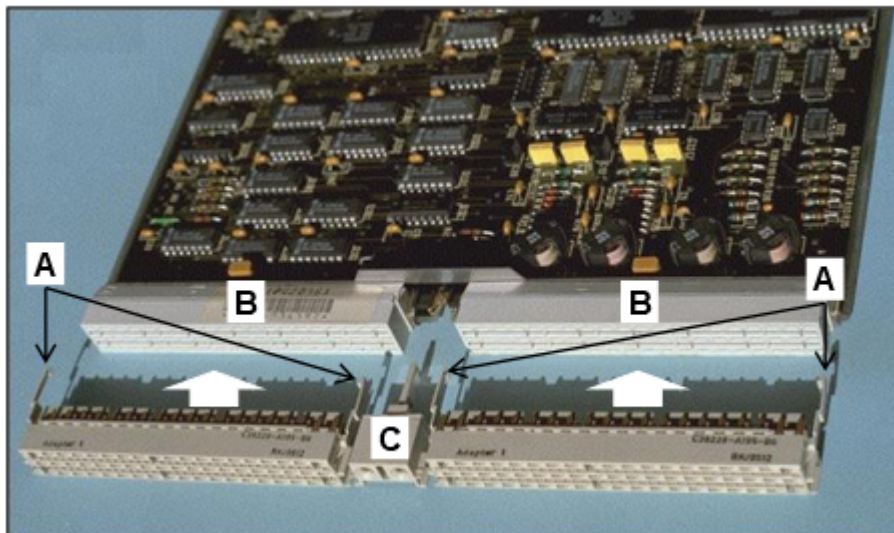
Montaje del adaptador de módulos SIVAPAC-SIPAC
